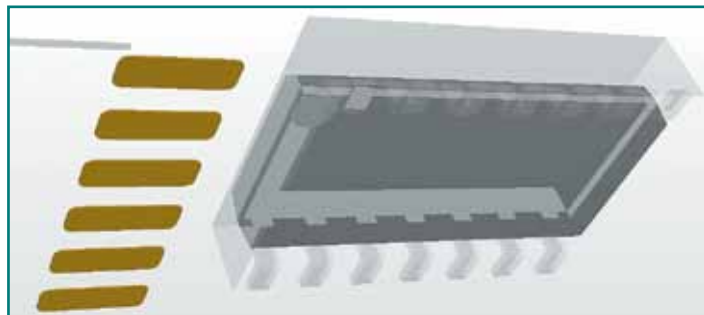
Выравнивание корпуса по верхней поверхности платы
